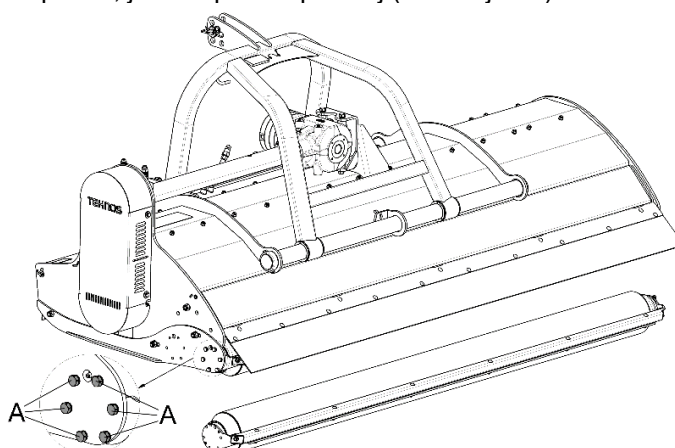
Pozycja zewnętrzna rolki wspierającej
